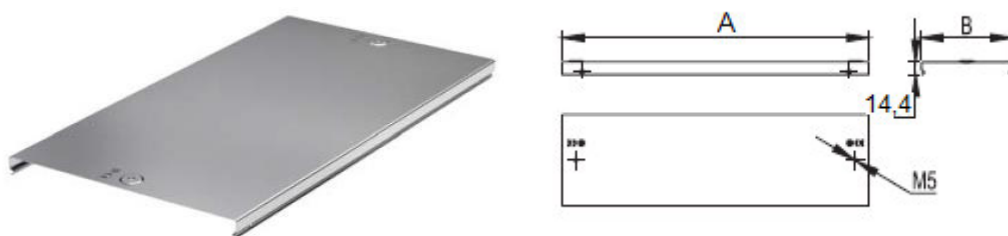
Крышка TDSA на ответвитель Т-образный вертикальный переходник, тип 3839
